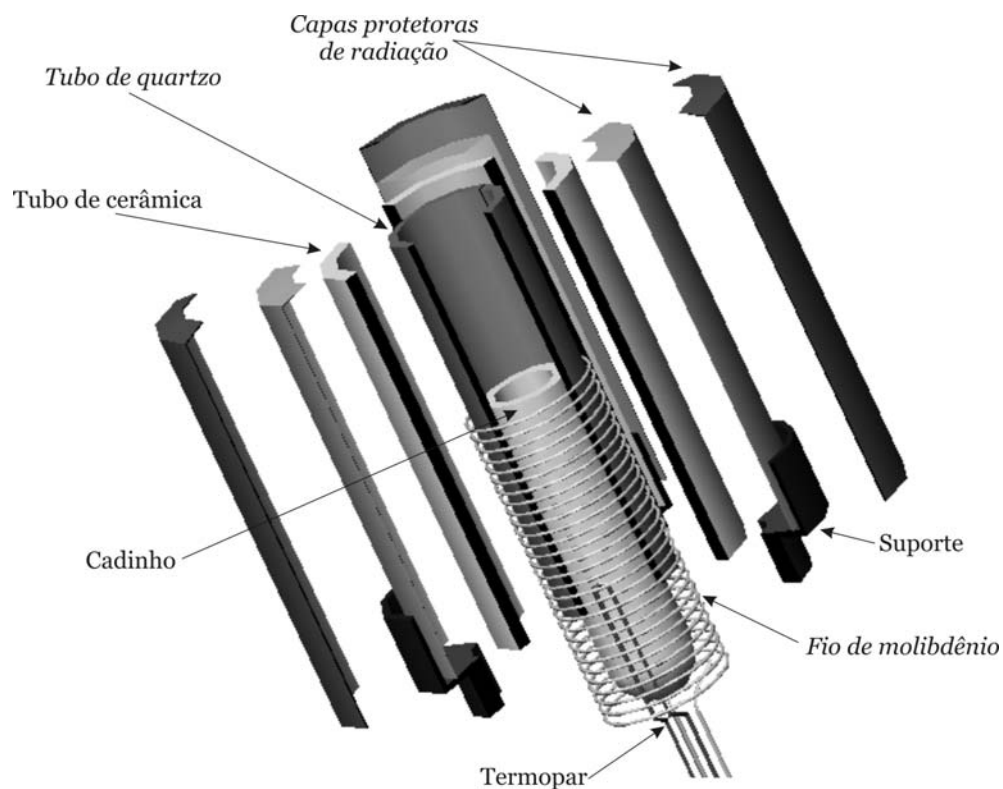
Vista explodida da célula de efusão projetada para o sistema de MBE.
